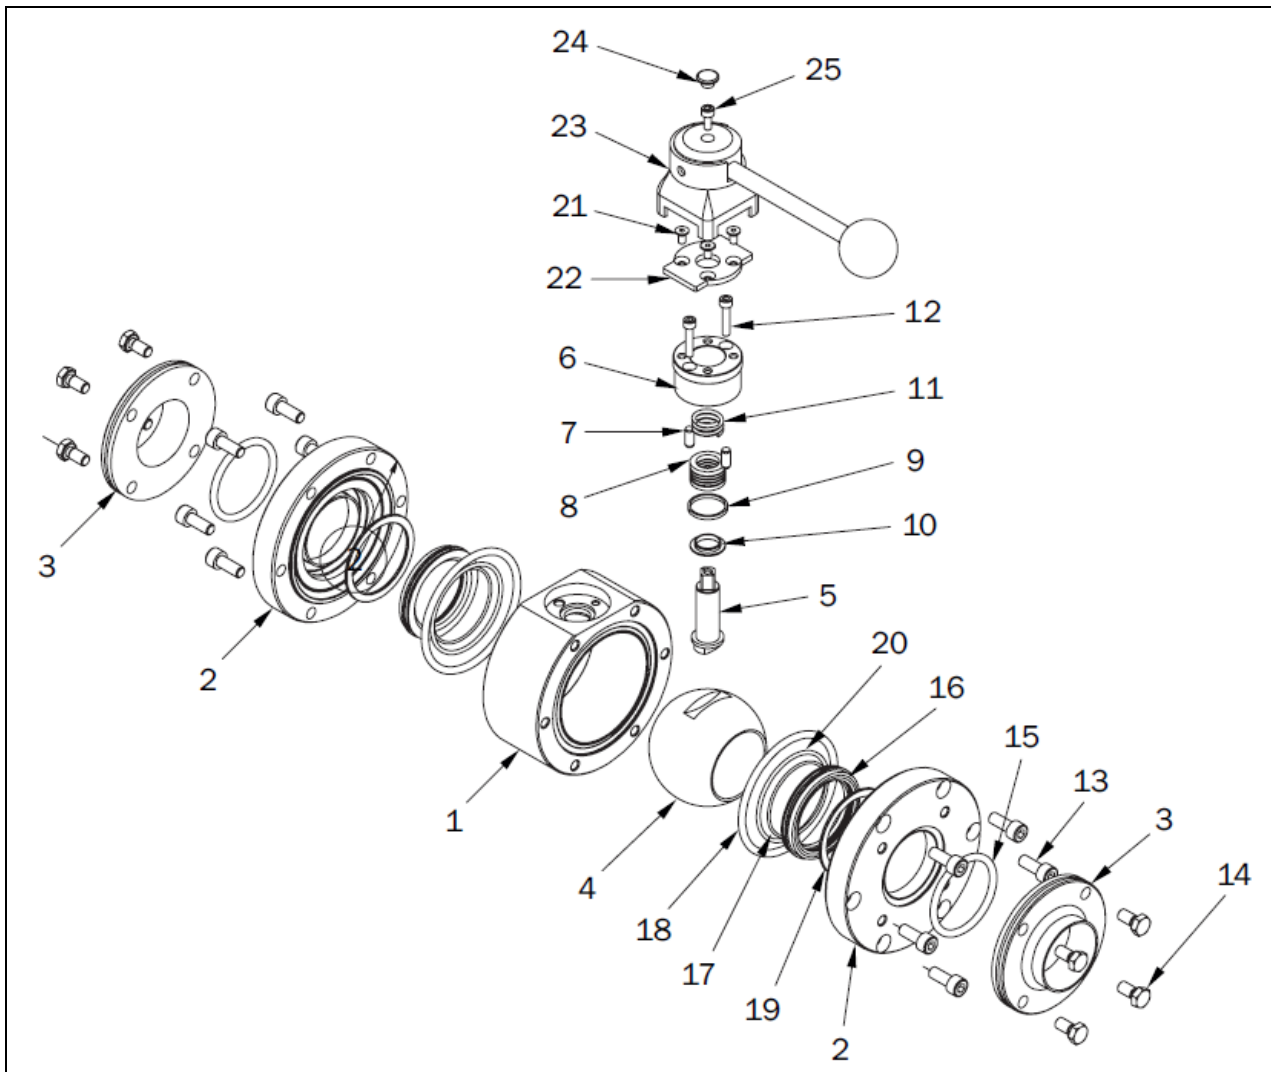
Aufbau Kugelventil mit Handgriff
